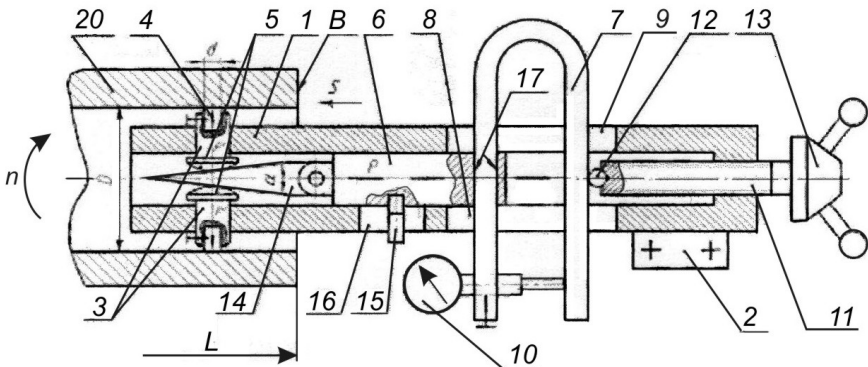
Пристрій для фінішної антифрикційної безабразивної обробки (ФАБО) внутрішніх циліндричних поверхонь
